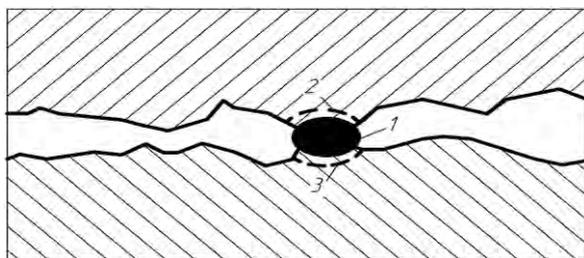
Схема образования схватывания контактирующих поверхностей: 1- локальный участок схватывания; 2,3 – линии границ разрушения металлических связей
